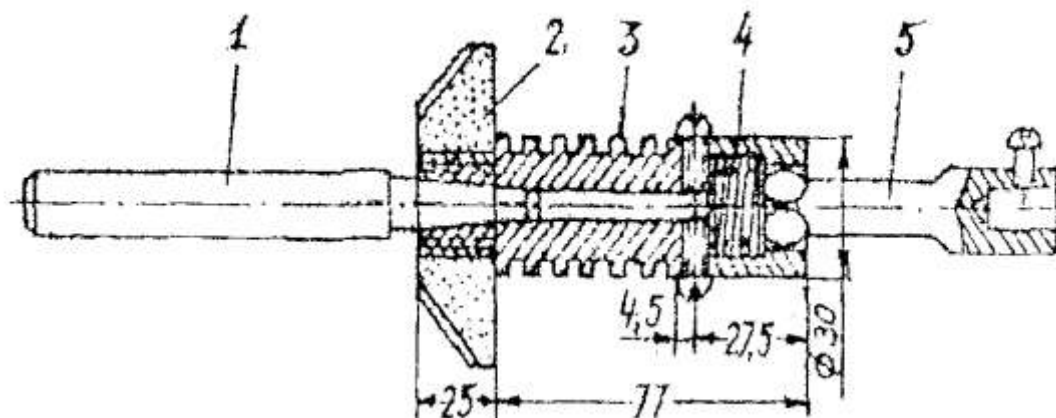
Приспособление для шлифовки гнезд абразивным наконечником:
